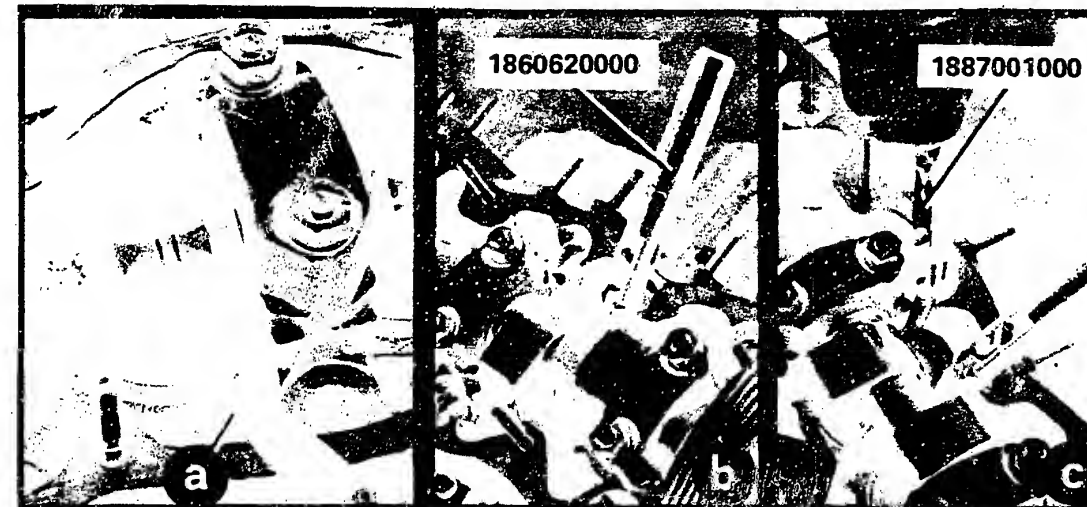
Motor 2500 turbo ds : Messen des Ventilspiels mit der Blattlehre (a) und Auswechseln der Einstellplättchen mit den Spezialwerkzeugen (b, c).
